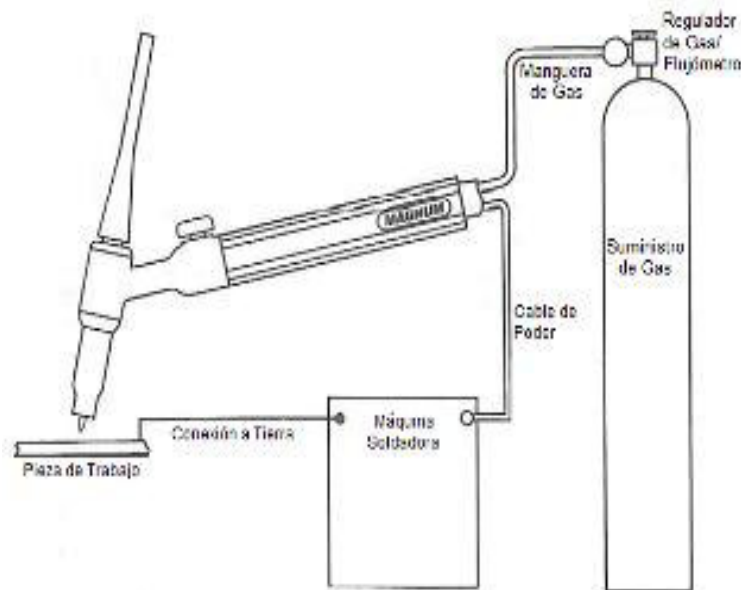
Configuración completa de la soldadura GTAW. [5]
